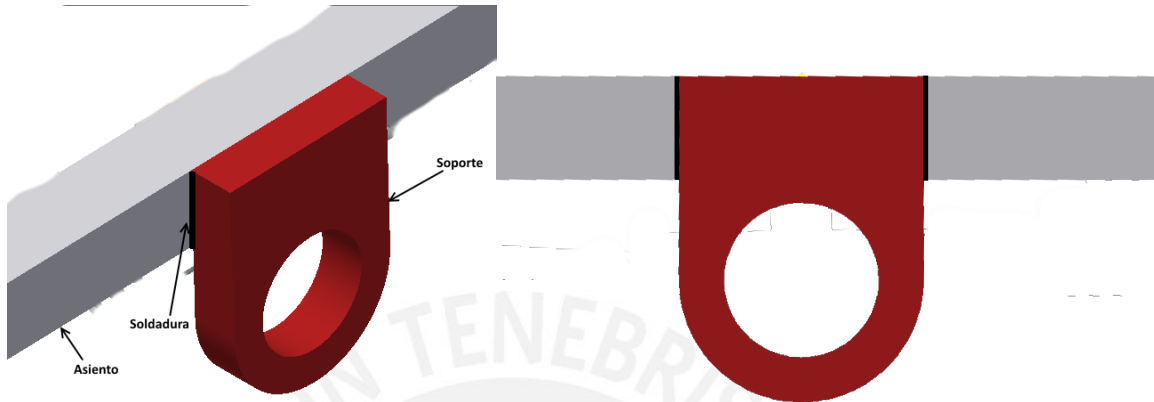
Ubicación de los cordones de soldadura
